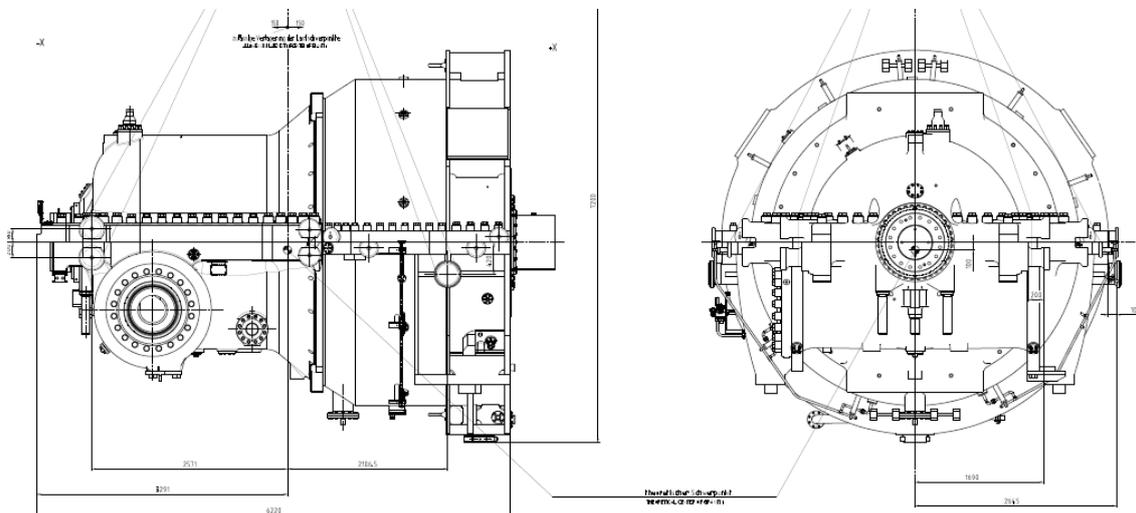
Plano al detalle de la turbina. Fuente: Marmedsa proyectos.
